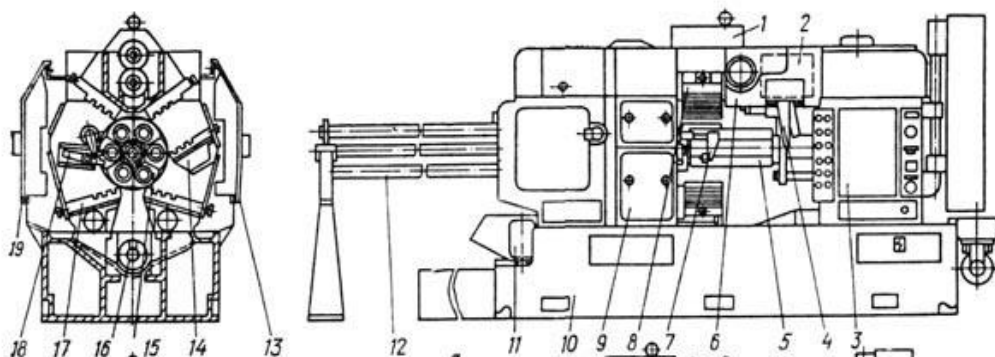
Розташування складових частин шестишпindelного токарного верстата 1Б240-6К : 1 – щити верхні; 2 – командо апарат; 3 – коробка передач; 4 – привід незалежних подач; 5 – супорт поздовжній; 6 – траверса; 7 – упор матеріалу; 8 – супорт верхній; 9 – механізми шпindelного блоку; 10 – станина; 11 – охолодження; 12 – труби напрямні; 13 – огорожа задня; 14 – супорт середній задній; 15 – барабан шпindelний; 16 – транспортер стружки; 17 – супорт нижній; 18 – супорт відрізний; 19 – огорожа передня [3].
